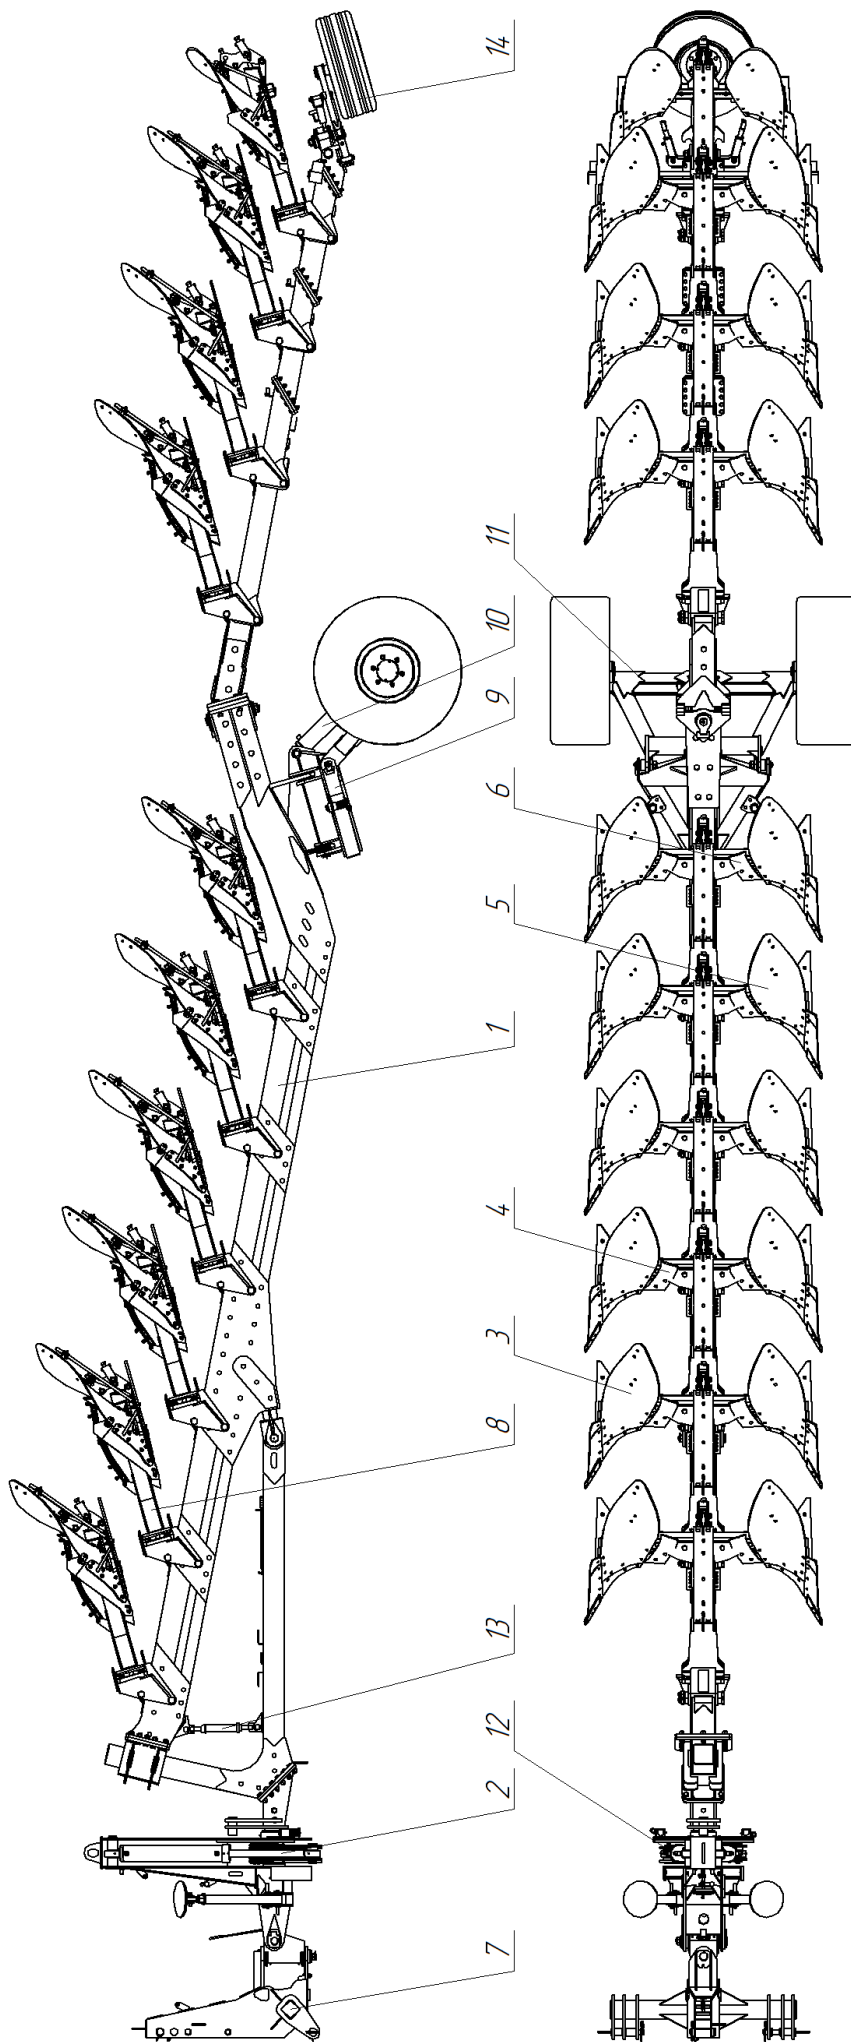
Плуг полунавесной оборотный девятикорпусный ППО-9-45К
